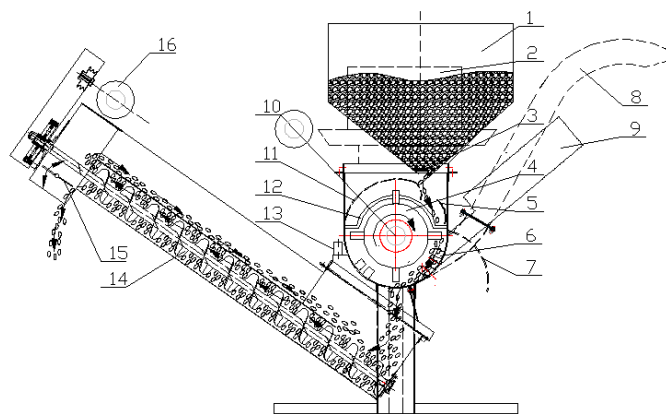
Схема универсального малогабаритного кормоприготовительного агрегата
